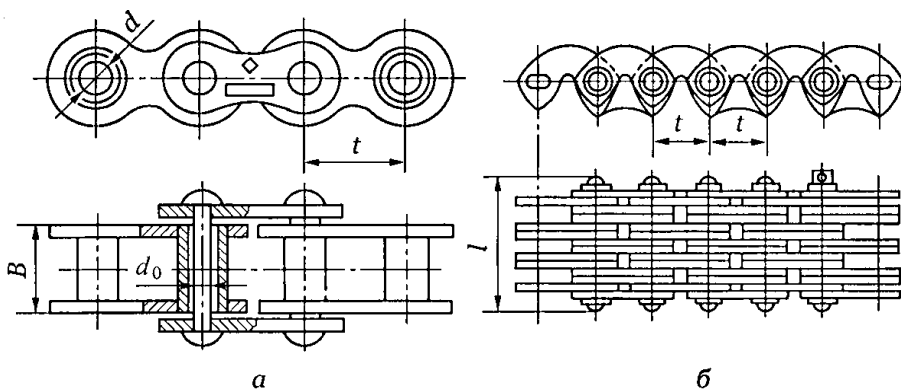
Типы цепей: а — втулочные; б — зубчатые
